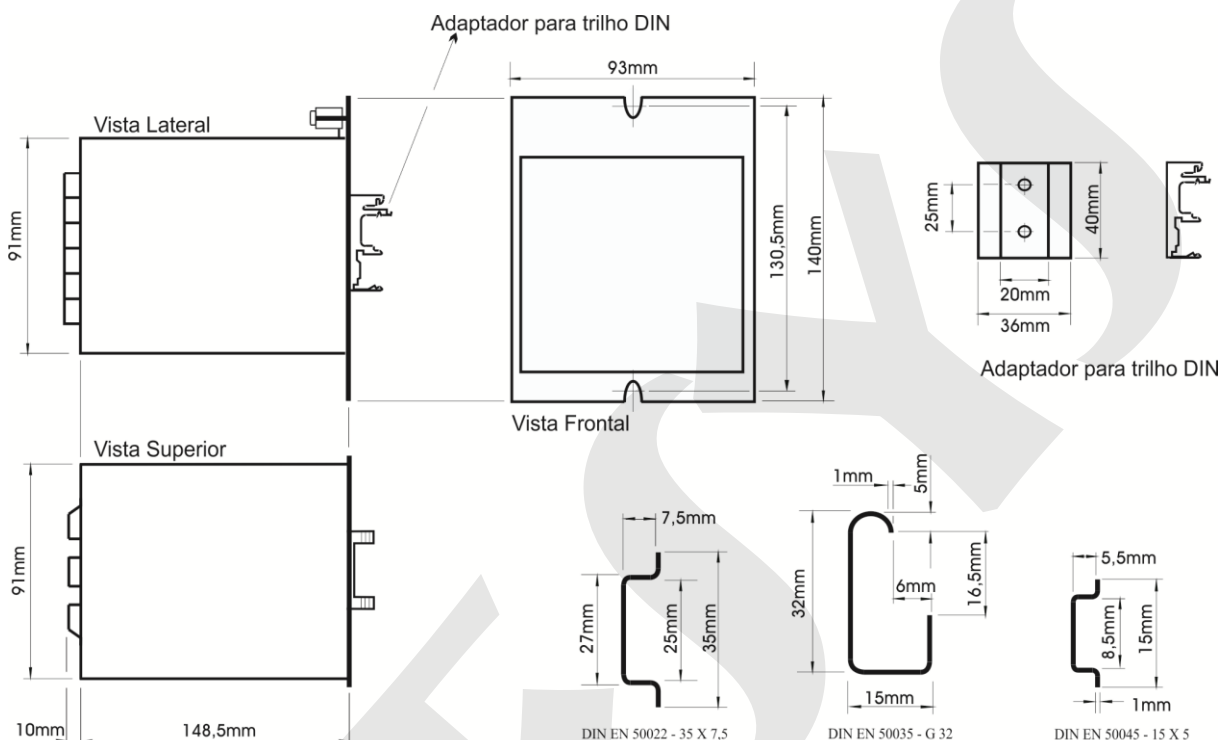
Desenho dimensional e detalhe do adaptador para trilho DIN
